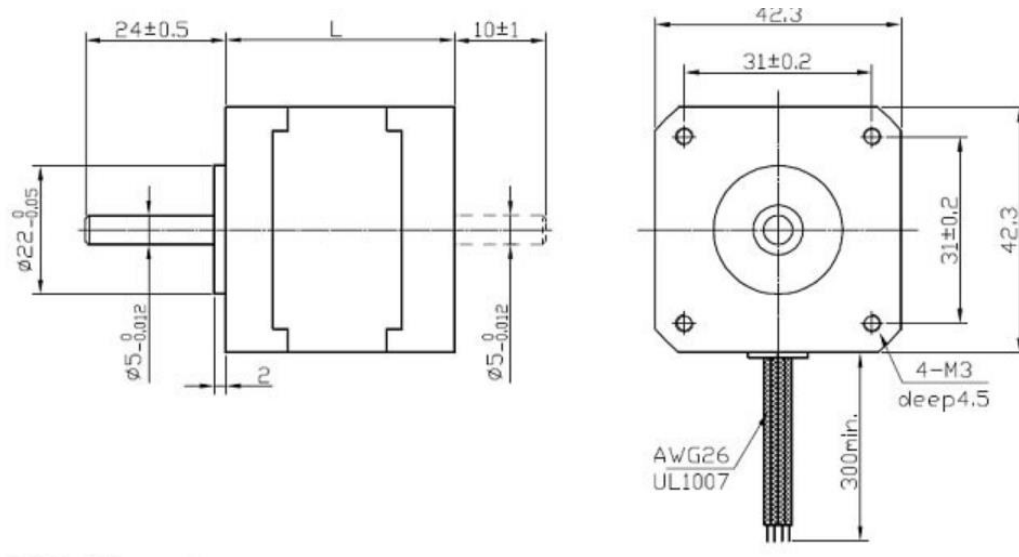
Dessin technique du moteur pas à pas nema 23
